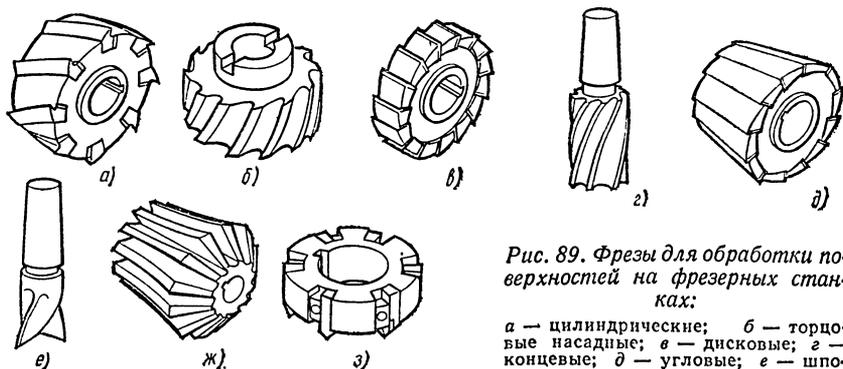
Фрезы для обработки поверхностей на фрезерных станках:
